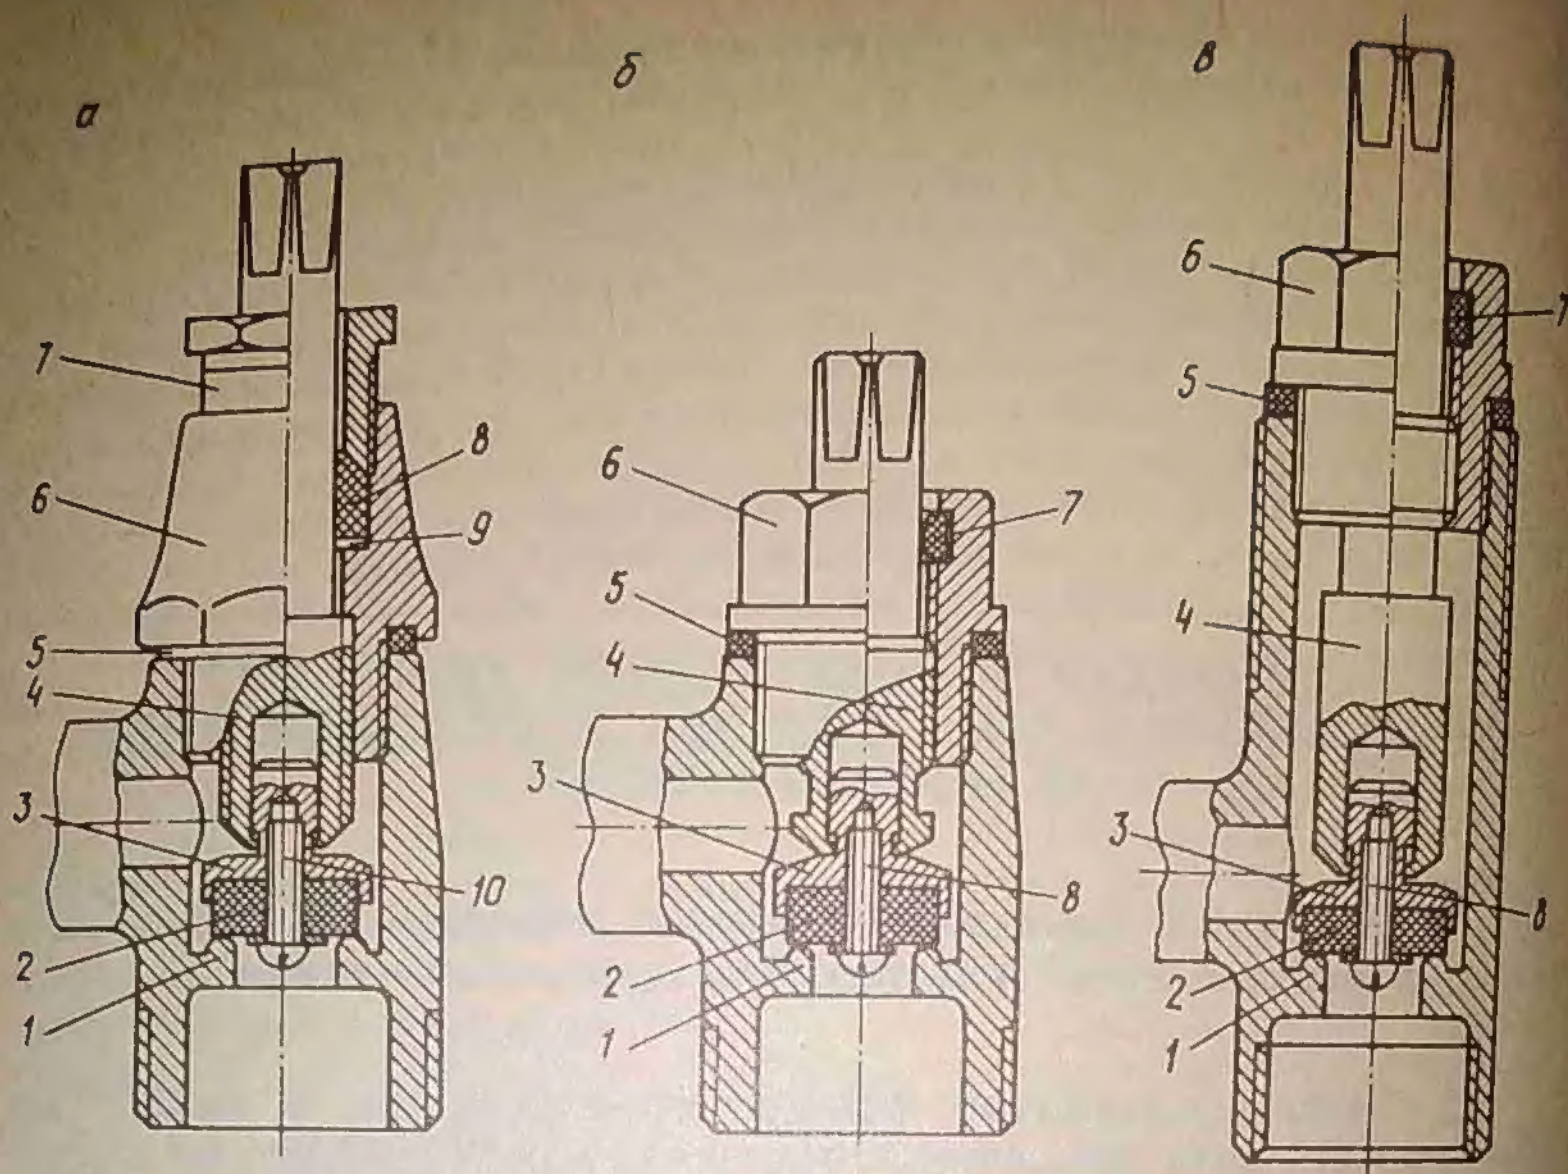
Вентильные головки вентиля с поворотно-поступательным движением клапана
